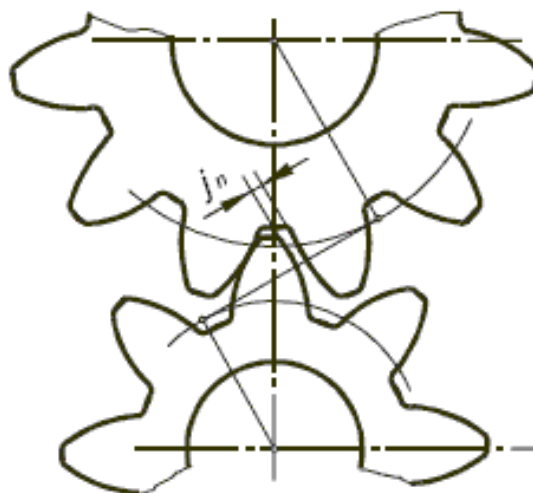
Боковой зазор  $j_n$  в зубчатой передаче
